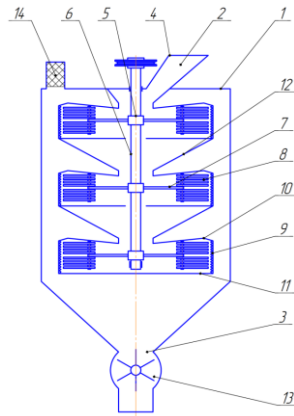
Багатоступенева дробарка: 1 – стінка корпусу; 2 - завантажувальний патрубок; 3 - отвір для розвантаження; 4 – бункер; 5 – ротор; 6 – вал приводний; 7 – диски розгінні; 8 – молоток; 9 – дека; 10, 11 – решето; 12 - похила поверхня; 13 - дозатор лопатевий; 14 – фільтрувальний елемент.
